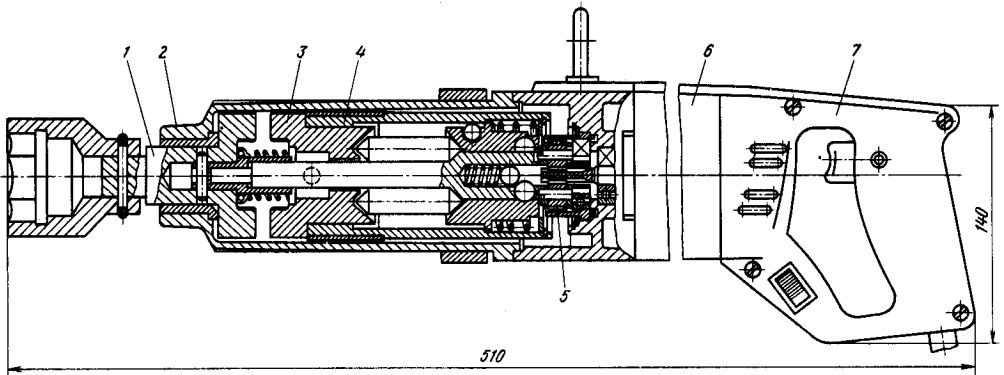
Гайковерт ИЭ-3119: 1 — шпиндель; 2 — корпус; 3 — ударно-вращательный механизм; 4 — корпус бойка; 5 — планетарный редуктор; 6 — электродвигатель; 7 — рукоятка
